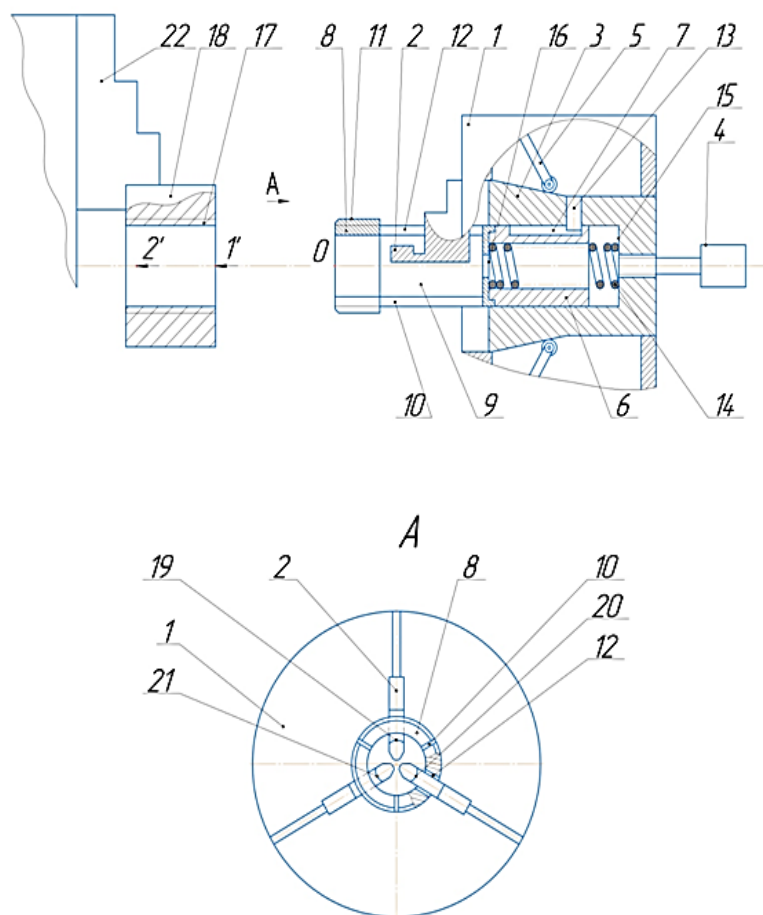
Патрон кулачковый механизированный для переустановки заготовки с резьбовым отверстием на станке
